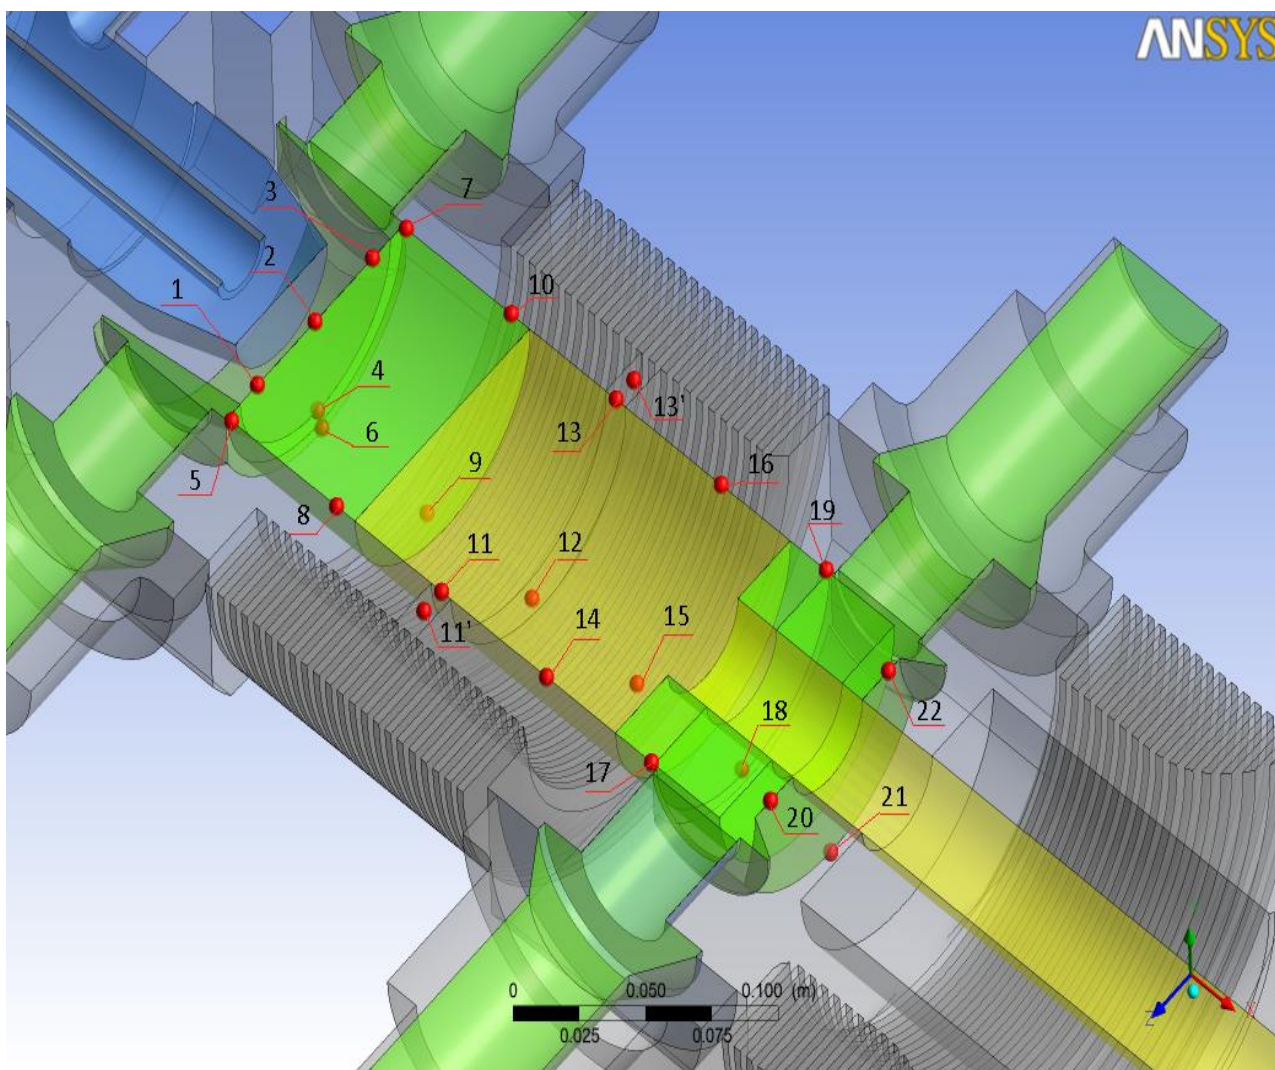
Контрольные точки в дожимающей ступени компрессора с поршнем двойного действия
